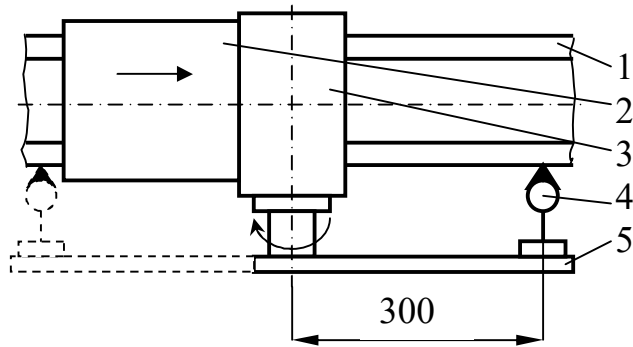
Схема перевірки неперпендикулярності осі шпинделя фрезерної бабки до напрямних силового столу: 1 – стіл; 2 – повзун столу; 3 – фрезерна бабка; 4 – індикатор; 5 - лінійка
